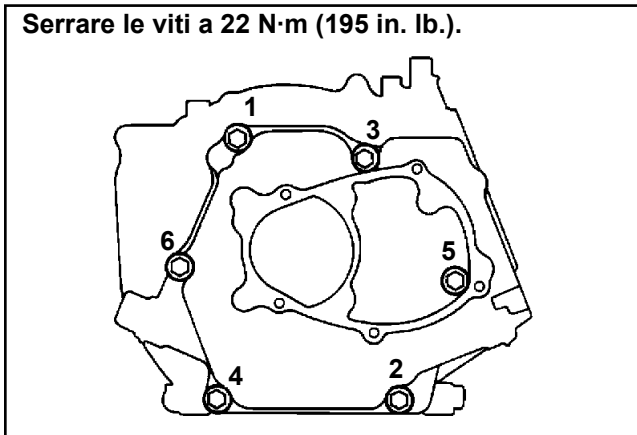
CS6 e CS4. Sequenza di serraggio della piastra di chiusura.
